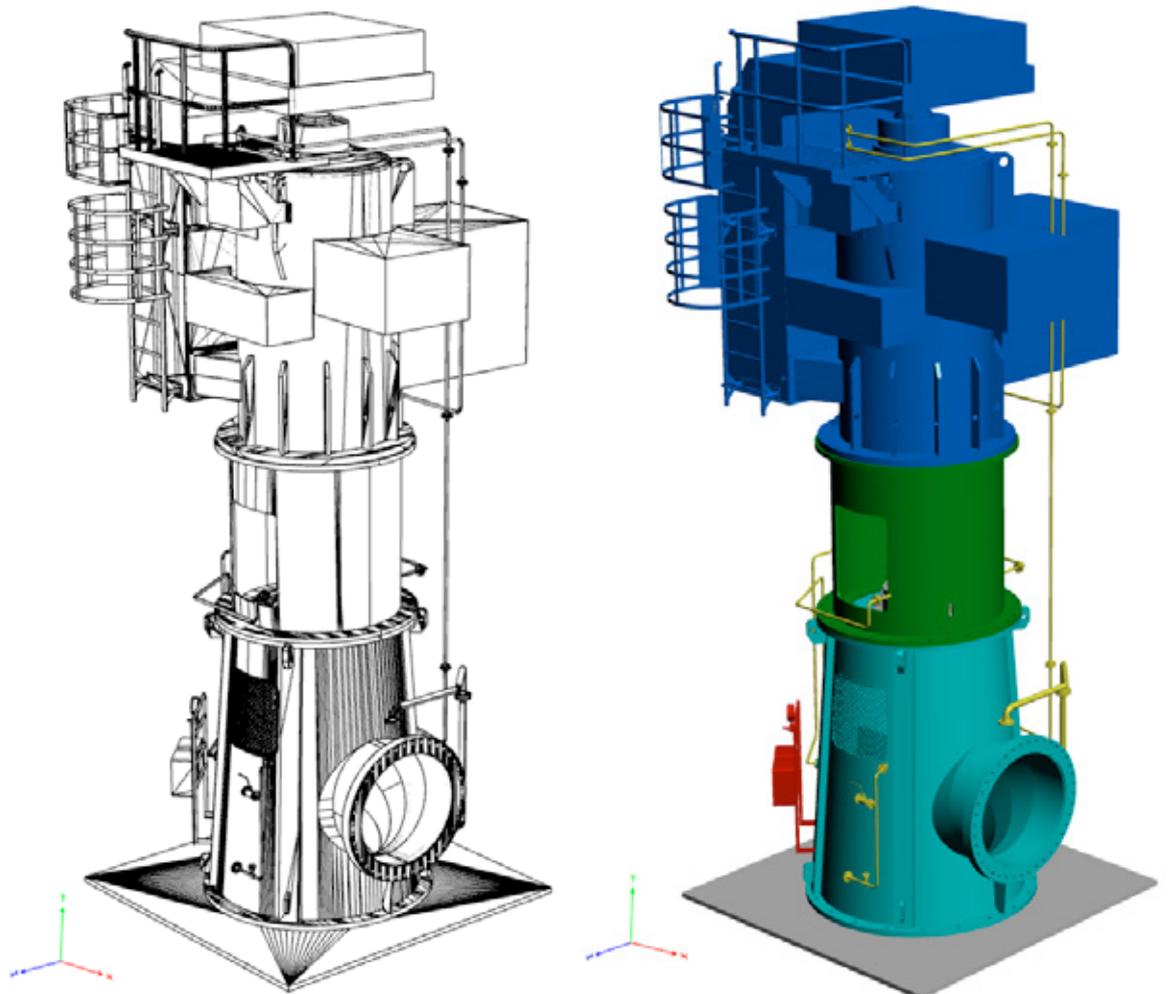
Pompa acqua mare "main": disegno 3D della parte superiore (non immersa)
